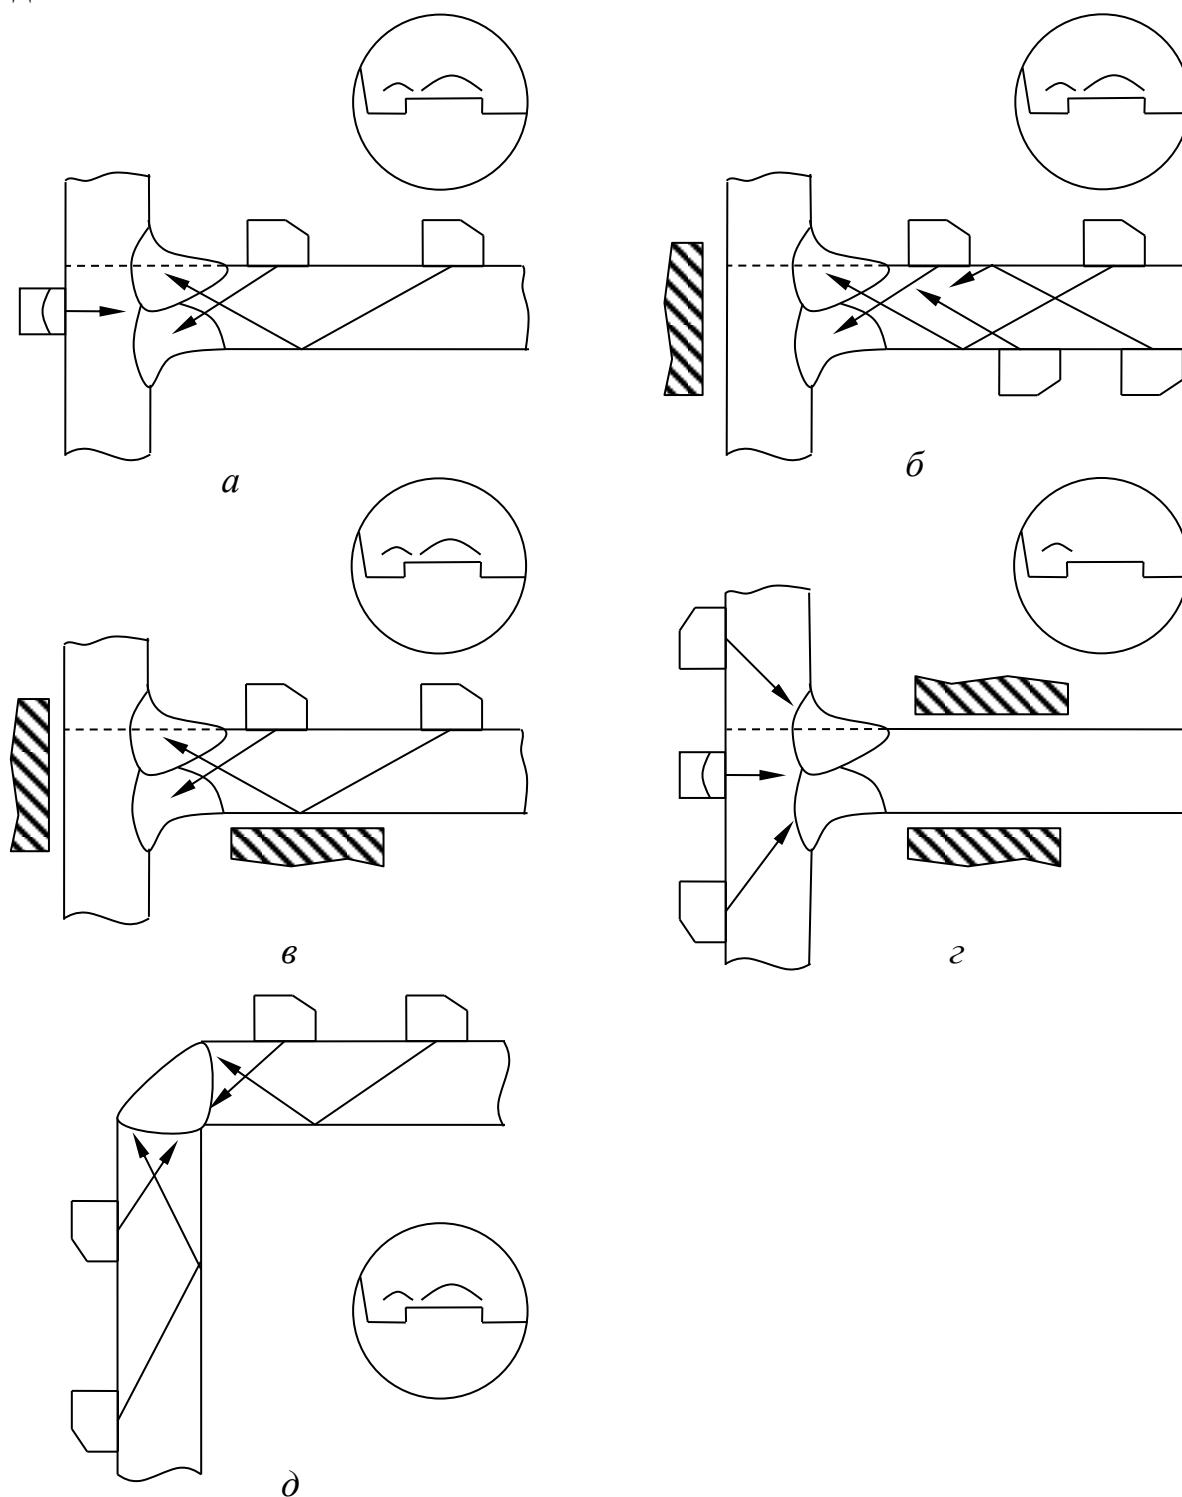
Схемы контроля тавровых и угловых сварных соединений
